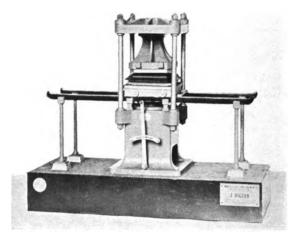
Machine à mouler. (V. Nº 11933.)
